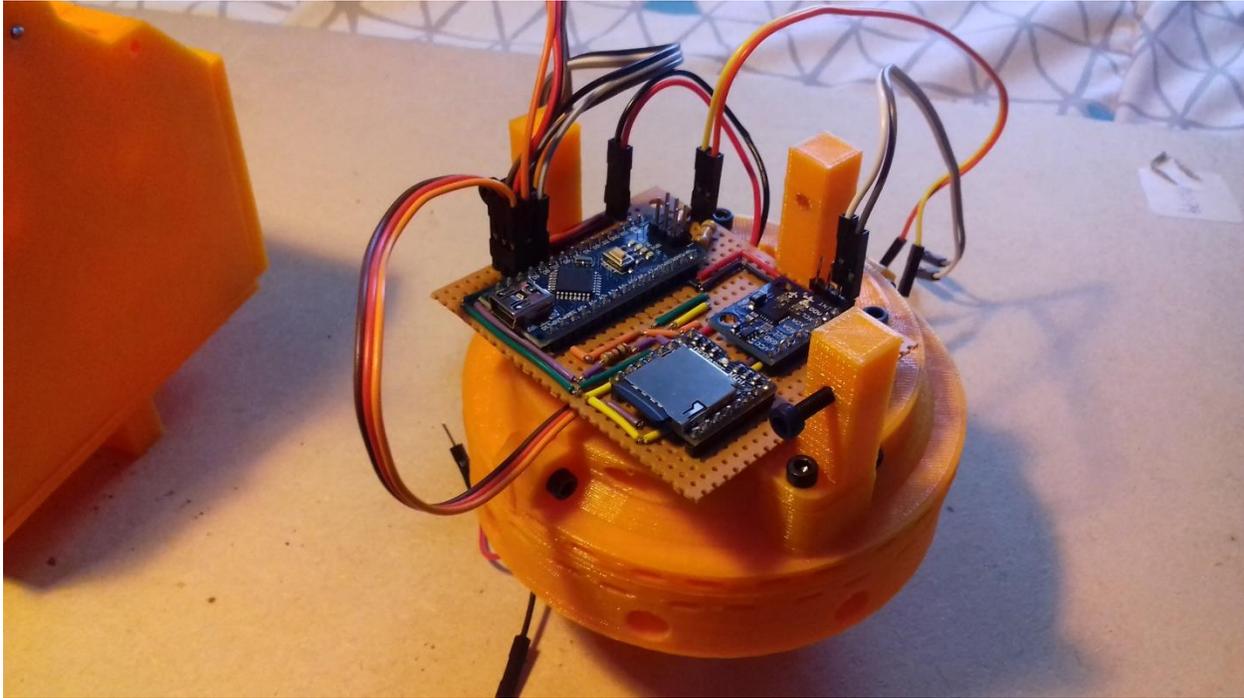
Placa electrónica siendo instalada en el esqueleto de peluche. Se observa también los distintos cables de sensores y actuadores siendo conectados a los pines header de la PCB.
